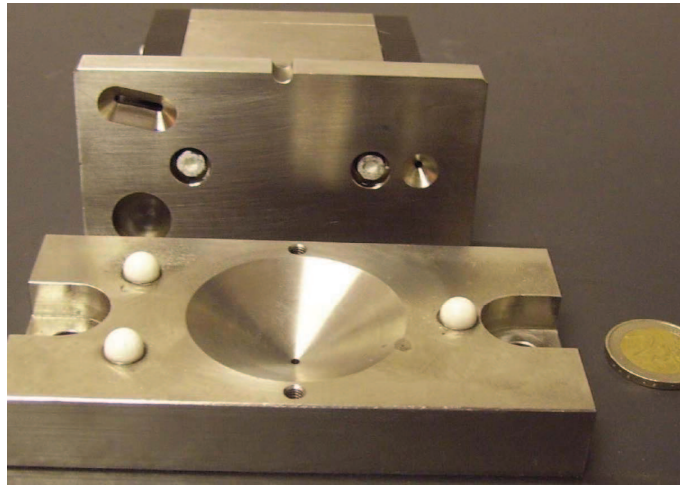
Centrage isostatique trait-point-plan sur trois billes
